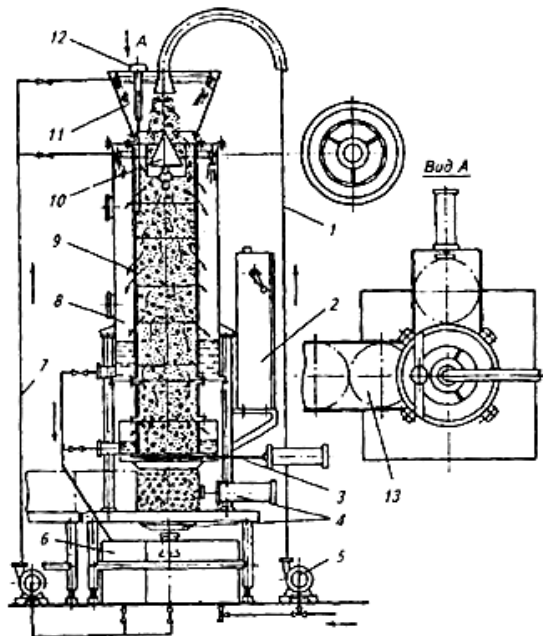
Формовочный аппарат РЗ-ОСО
